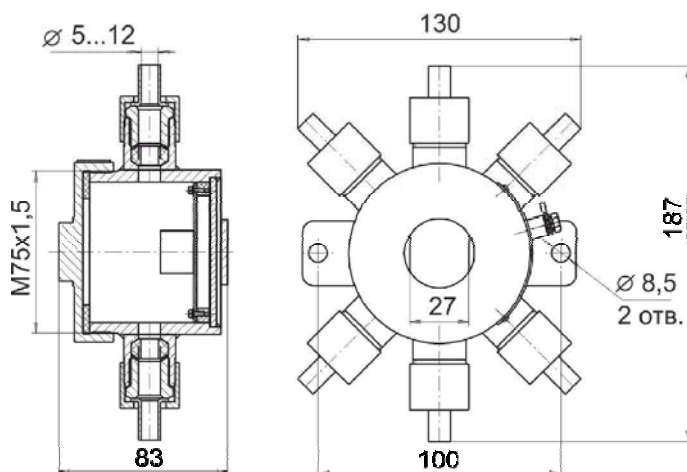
Коробка ВУУК. Габаритные и установочные размеры.
